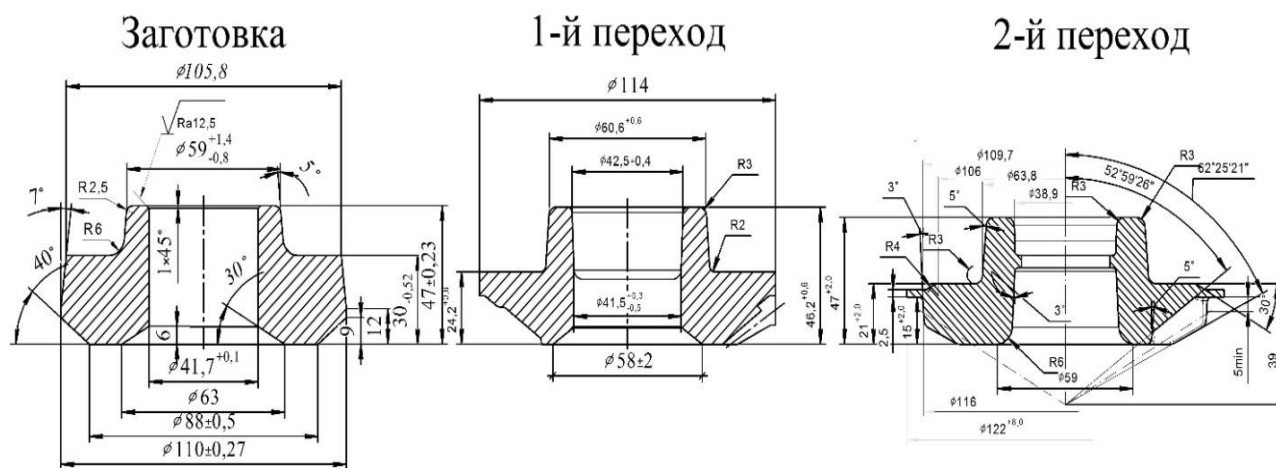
Переходы сферодвижной штамповки конического зубчатого колеса
